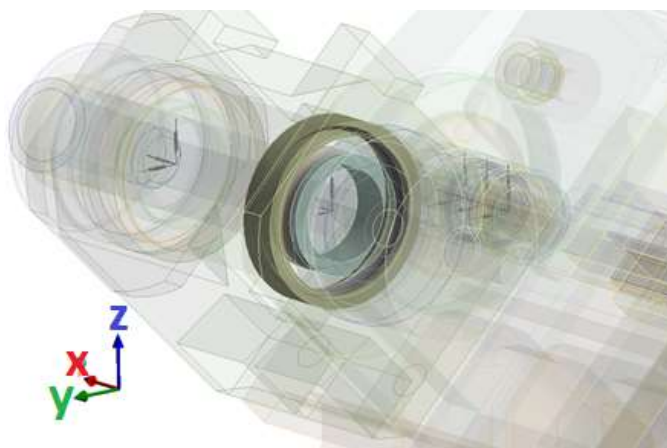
Підшипник передньої бабки токарного верстат
